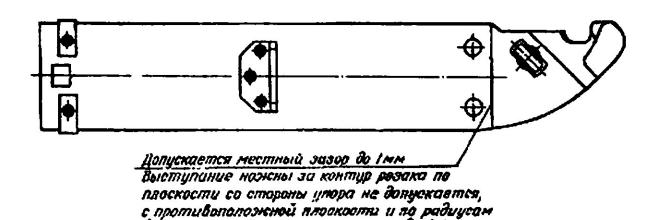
Устранение качки резака и соединении с корпусом ножны: 49 - корпус пожны; 59 — резак; 59 — заклепка
